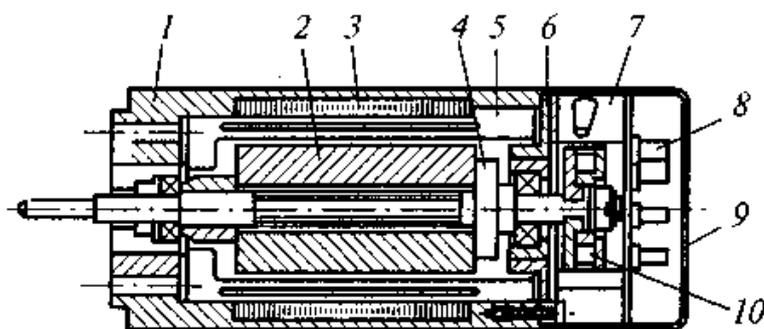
Бесконтактный исполнительный двигатель типа ДБУ:
